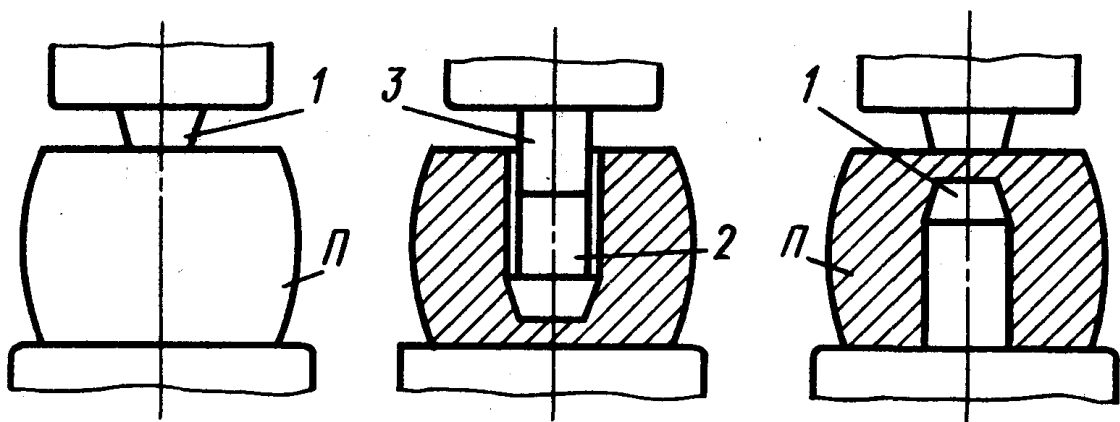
Схема прошивання без підкладного кільця: 1 – прошивка; 2 – перша надставка; 3 – друга надставка; П – збільшена частина заготовки
